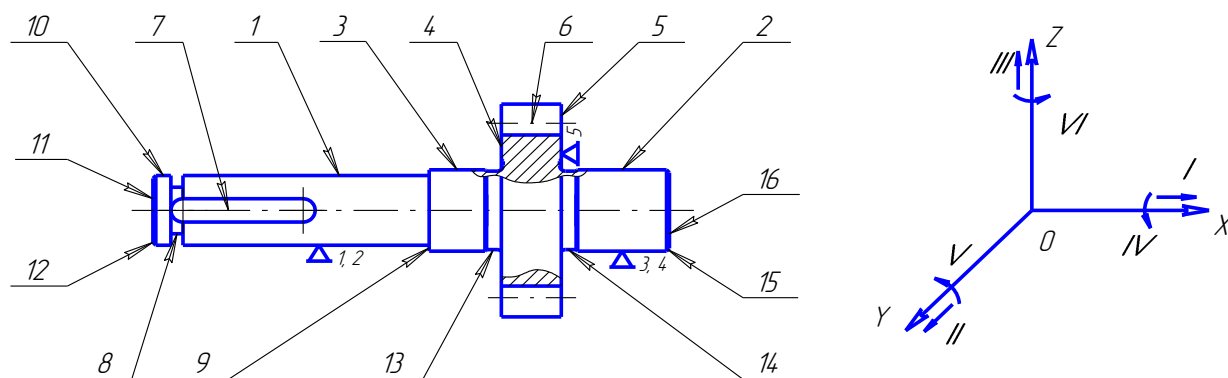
Ескіз деталі "Вал-шестерня"
